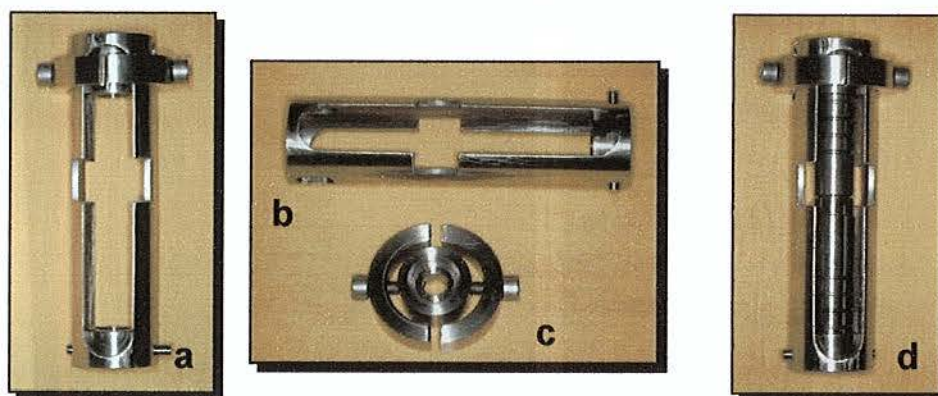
Dispositivo desenvolvido para manter os corpos-de-prova em posição e sob pressão constante de assentamento. a) dispositivo montado; b) corpo; c) êmbolo que desliza no interior do corpo, com dois parafusos para fixação; d) dispositivo montado, com um corpo-de-prova no seu interior.
